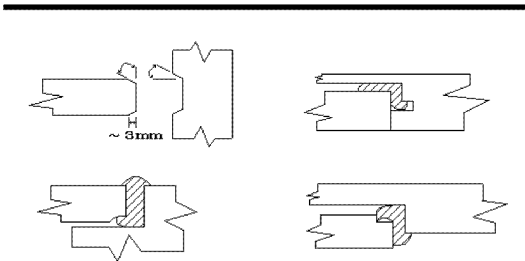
Recesso nas Partes Soldadas para Permitir o Escoamento do Material.
